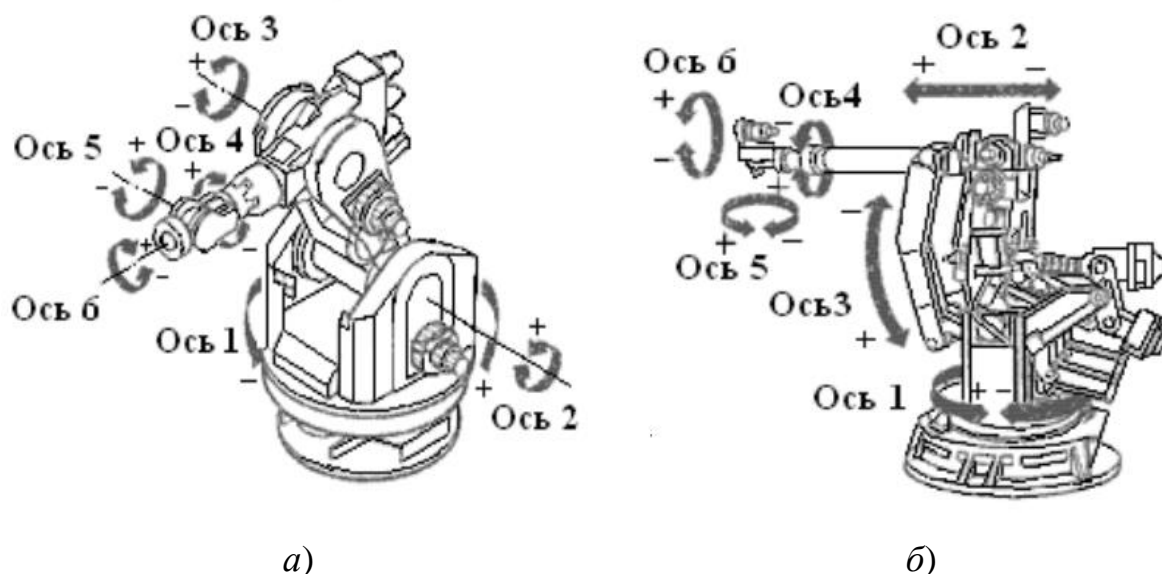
Степени подвижности сварочных роботов типа: а) IR-160/60 и б) IR -601/60 немецкой фирмы «Kuka»
